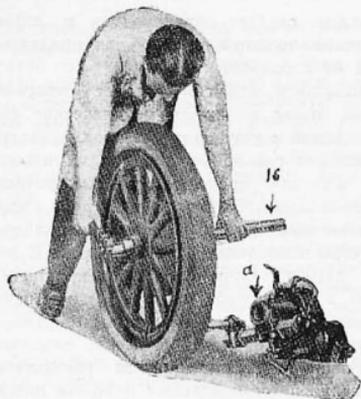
Затяжка центрального шпинделя во втулке ступицы колеса
